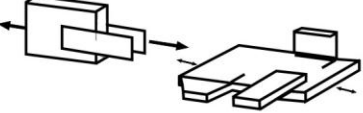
Roturas por fadiga em juntas transversais com penetração parcial do cordão de soldadura [70]:
